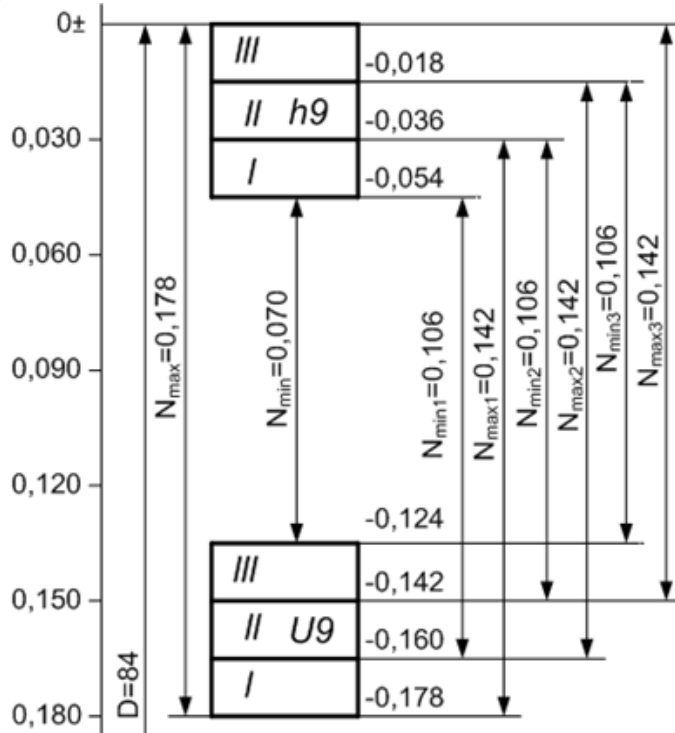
Схема розташування полів Допусків з'єднання Ø84U9/h9
